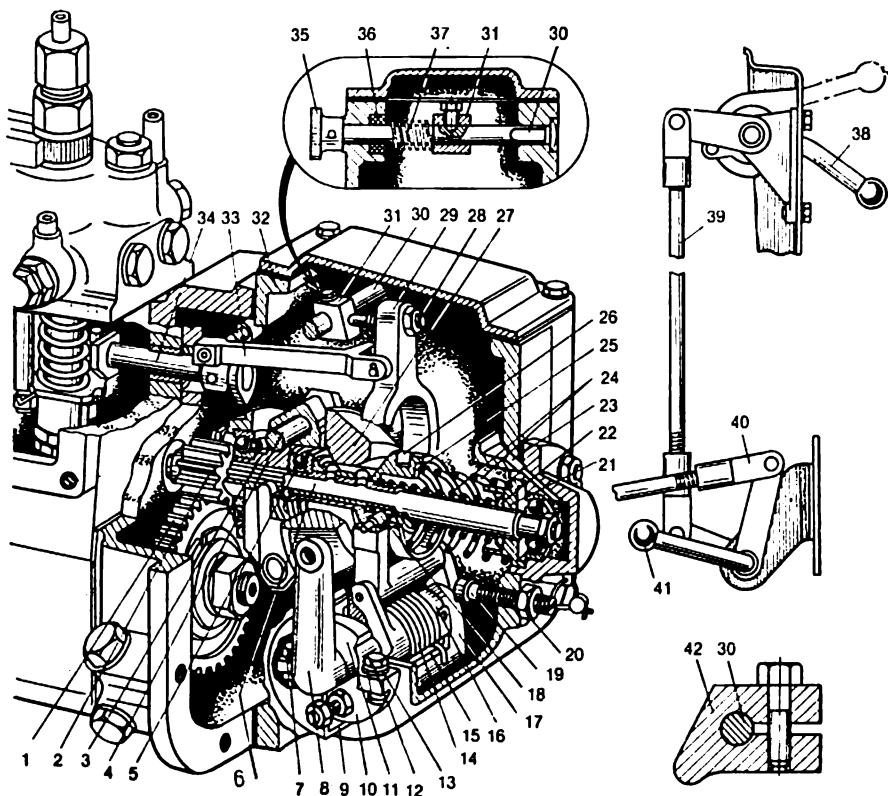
Régulateur tous régimes du moteur Diesel A-41:
